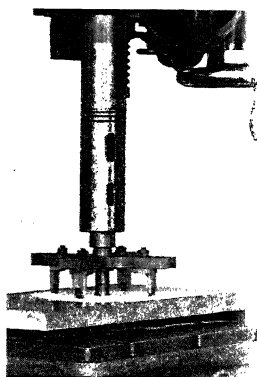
Ausschneiden von Marmor mit radial verstellbarem Ausstechwerkzeugen.
